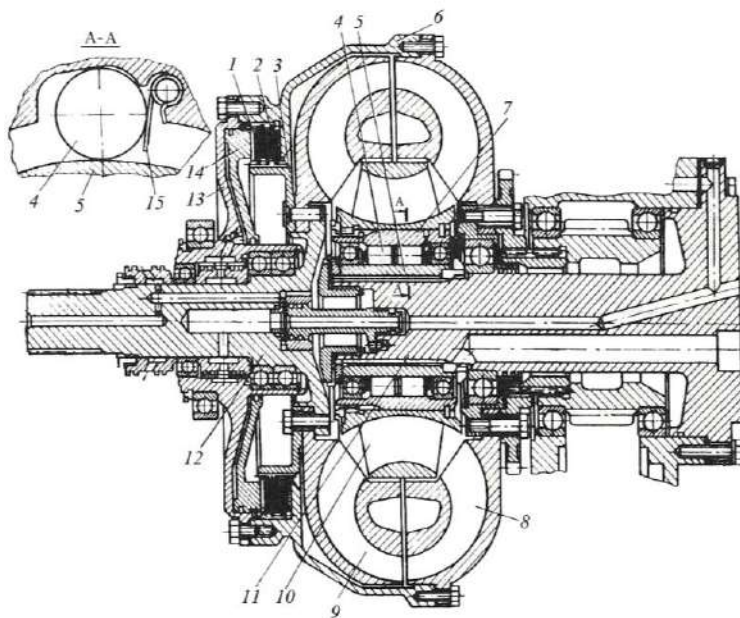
Гідротрансформатор: 1 – ведучий металокерамічний диск; 2 – ведучий сталевий диск; 3 – маточина фрикціона блокування; 4 – ролик, що заклинює круглий рух; 5 – внутрішня обойма муфти; 6 – корпус; 7 – зовнішня обойма муфти; 8 – насосне колесо; 9 – турбінне колесо; 10 – реактор; 11 – ось гідротрансформатора; 12 – турбінний вал; 13 – кришка; 14 – поршень; 15 – підтискна пружина
